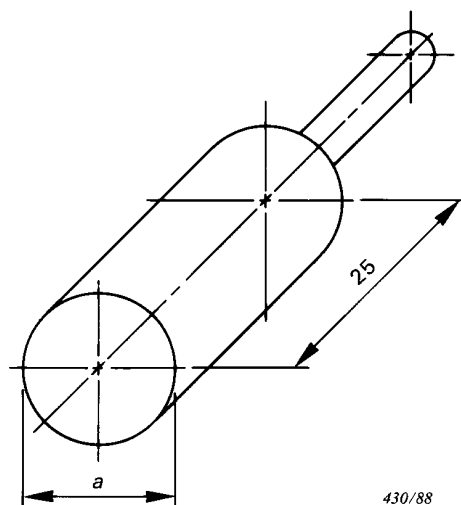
Arrangement et dimensions des électrodes pour l'essai de résistance aux courants de cheminement
